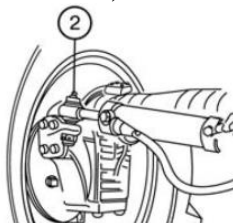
Шарнир крепления гидроцилиндра ГОРУ
